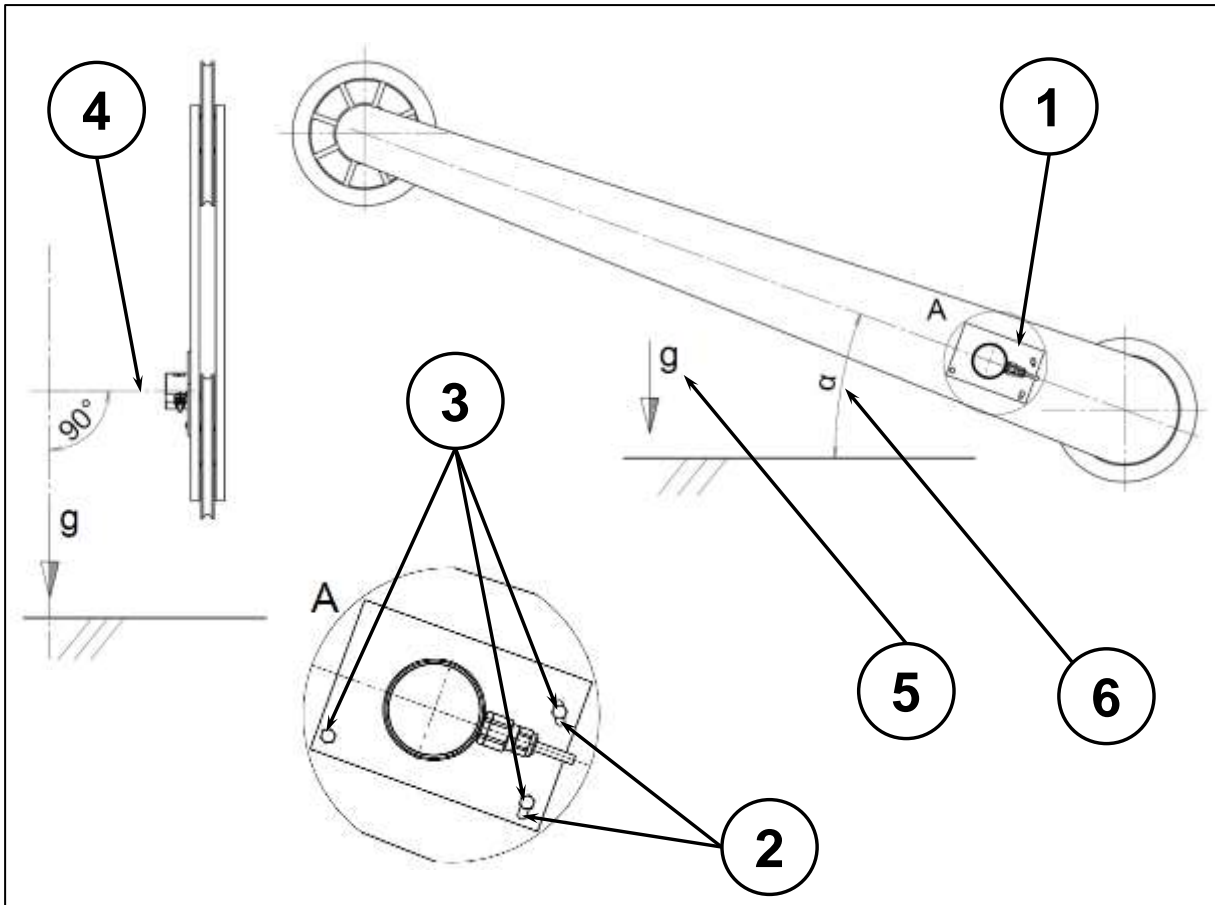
Rapporti di installazione, ad esempio per il braccio di una gru
